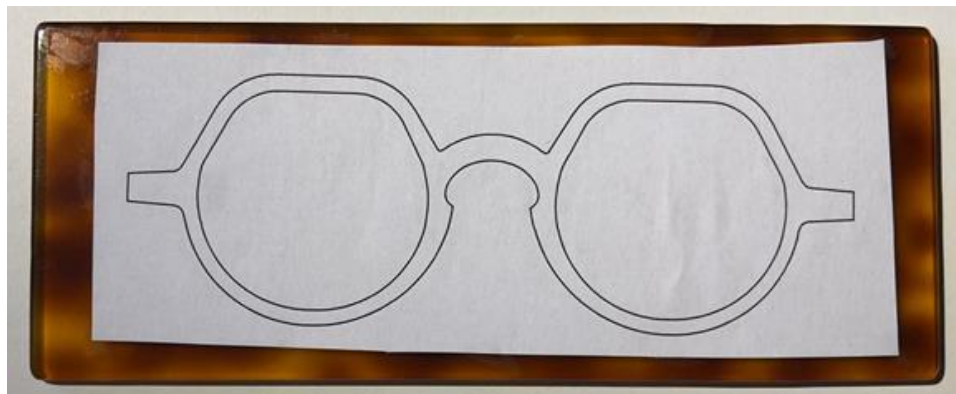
Impressió del frontal enganxat a la placa d'acetat
